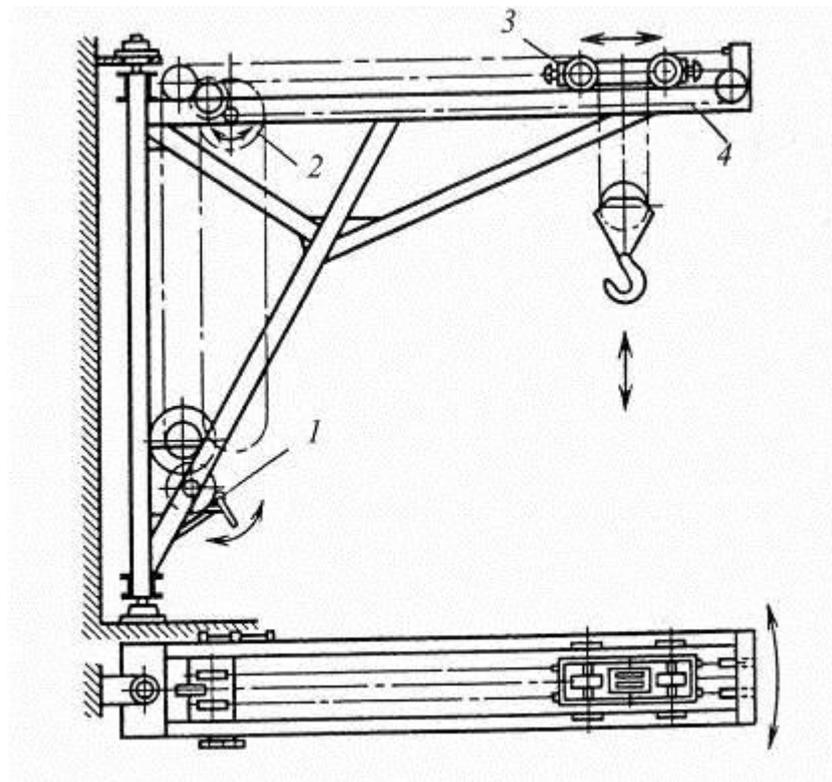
Консольный настенный поворотный кран с переменным вылетом и ручным приводом: 1 — лебедка; 2 — цепное колесо; 3 — тележка; 4 — канат
